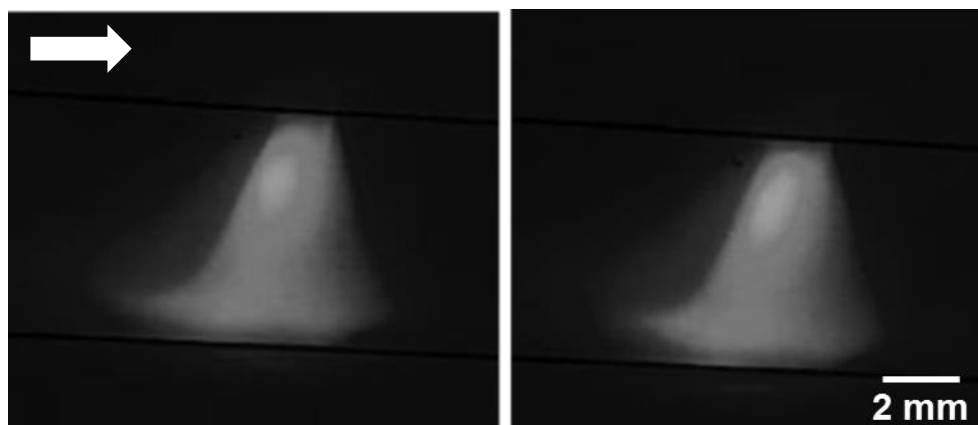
Imagens do arco elétrico da soldagem MIG a 190A. A direção de soldagem é indicada pela seta.
